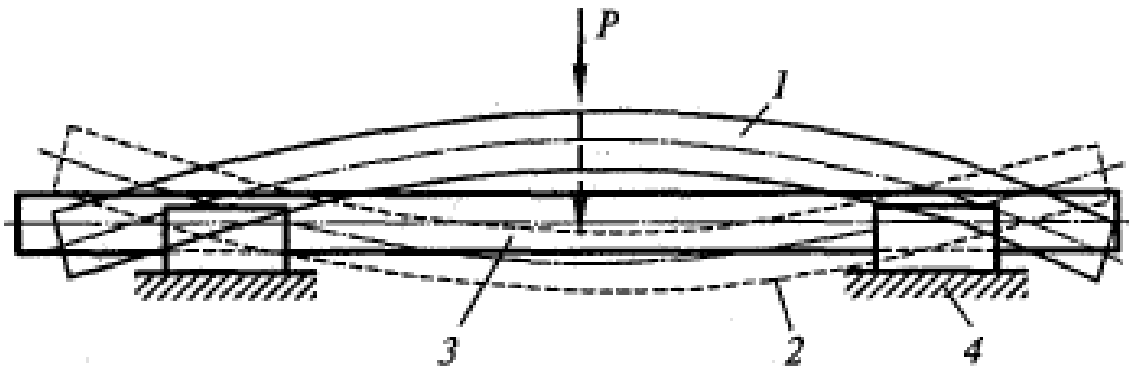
Схема правки прутка на двох опорах: 1 і 2 – пруток в процесі правки; 3 – пруток після правки; 4 – опорні призми
